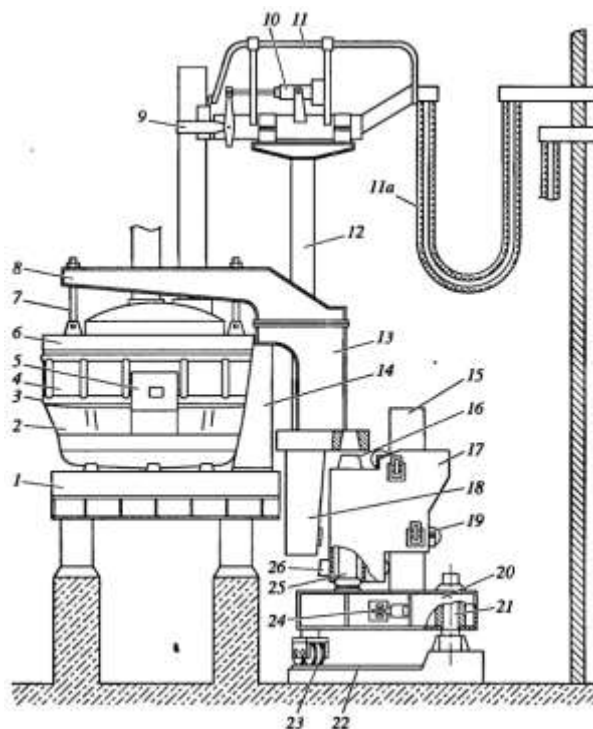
Печь с опорой механизмов подъёма — поворота свода на отдельный фундамент
